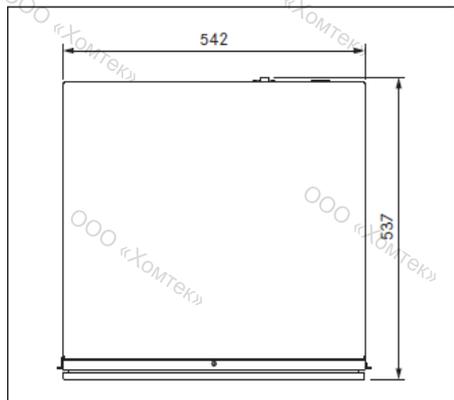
Размеры прибора, модель MS140, вид сверху
